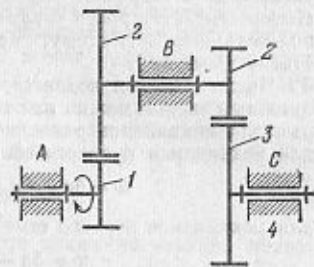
Двухступенчатый редуктор с цилиндрическими зубчатыми колесами.
